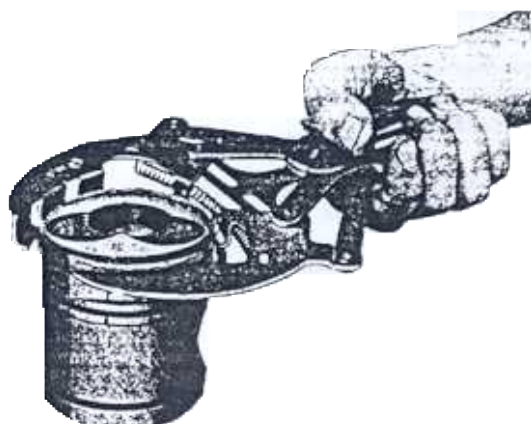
A-12G-03 — Montaje y desmontaje de segmentos
